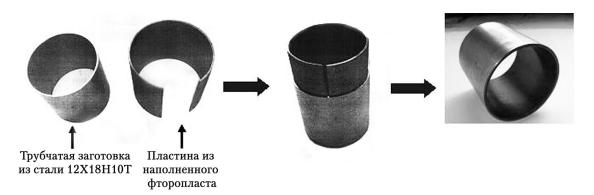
Схематическое изображение последовательности изготовления двухслойной фторопластсодержащей втулки
